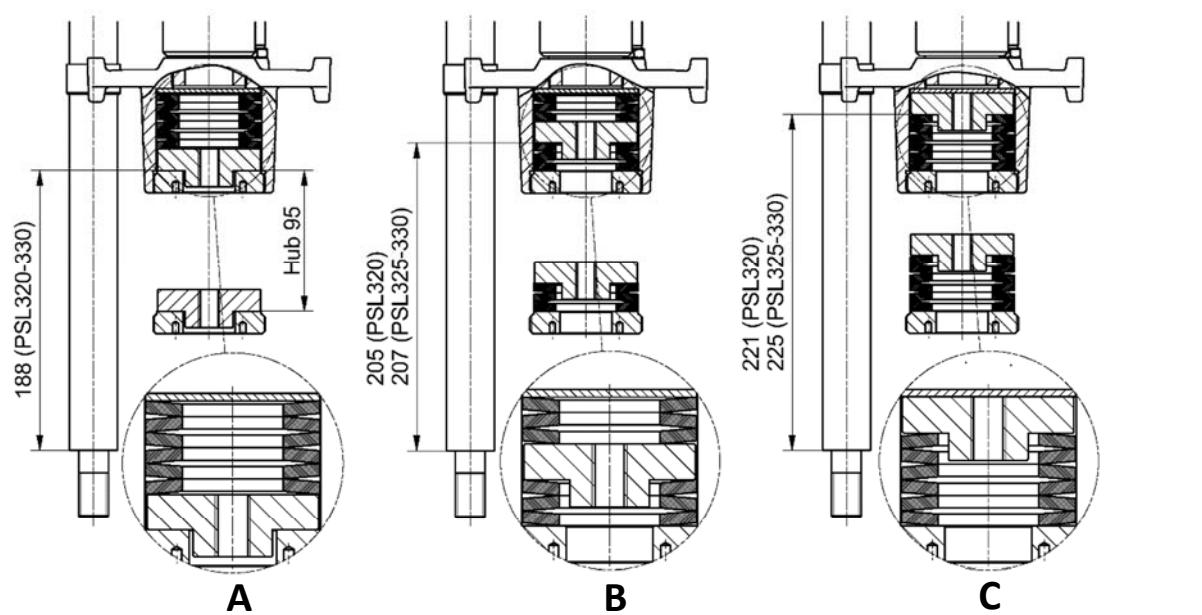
Стандартный соединительный элемент с дисковой пружиной
